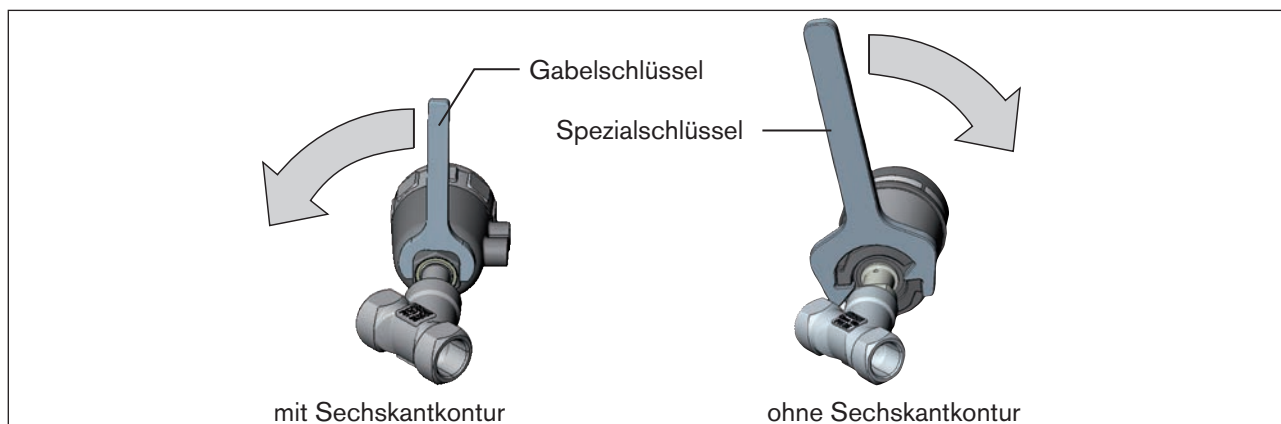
Drehen mit Speziesschlüssel / Gabelschlüssel
